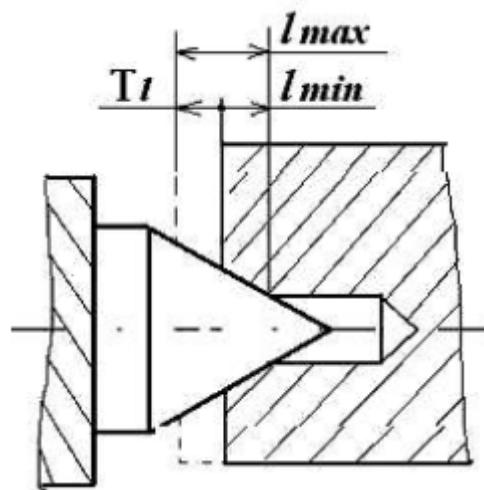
Конструкція опорної поверхні твердого центру
